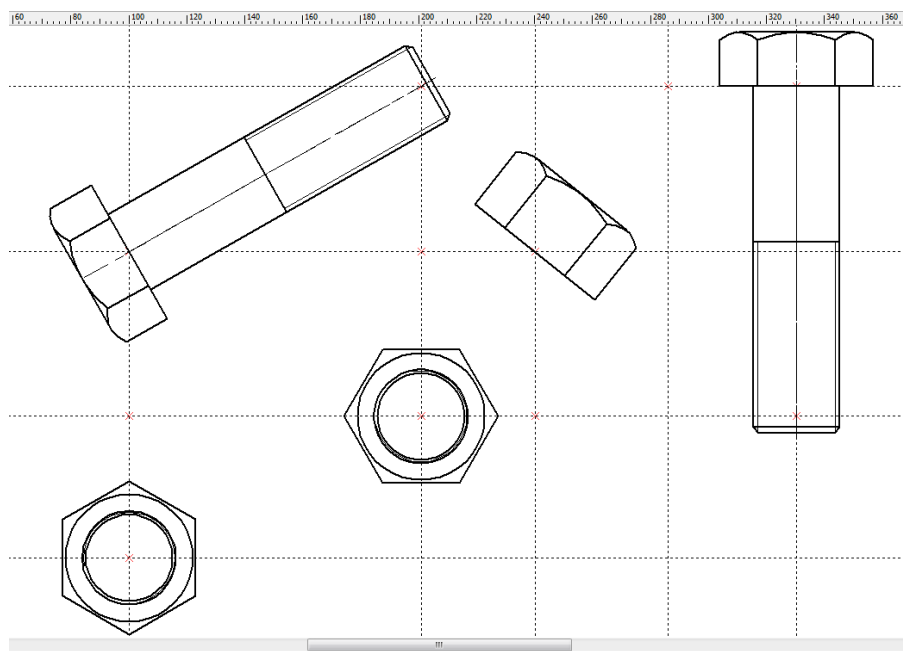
Расположение фрагментов на сборочном чертеже
